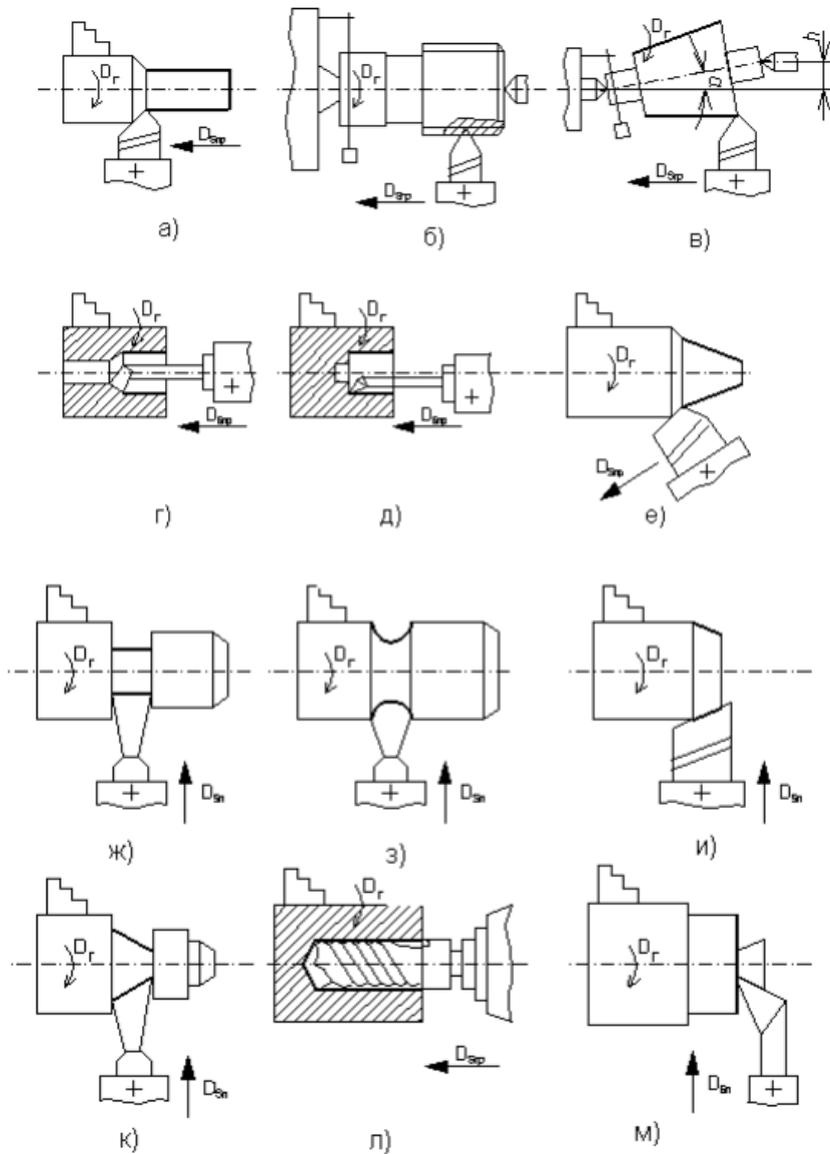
Схемы обработки поверхностей заготовок на токарно-винторезных станках
